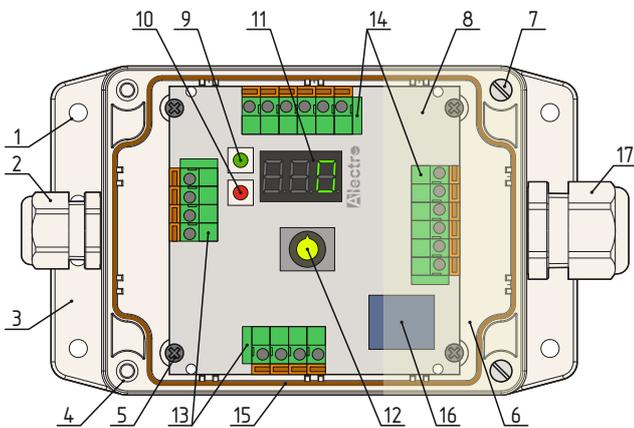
Конструкция устройства контроля скорости SCD-01.
